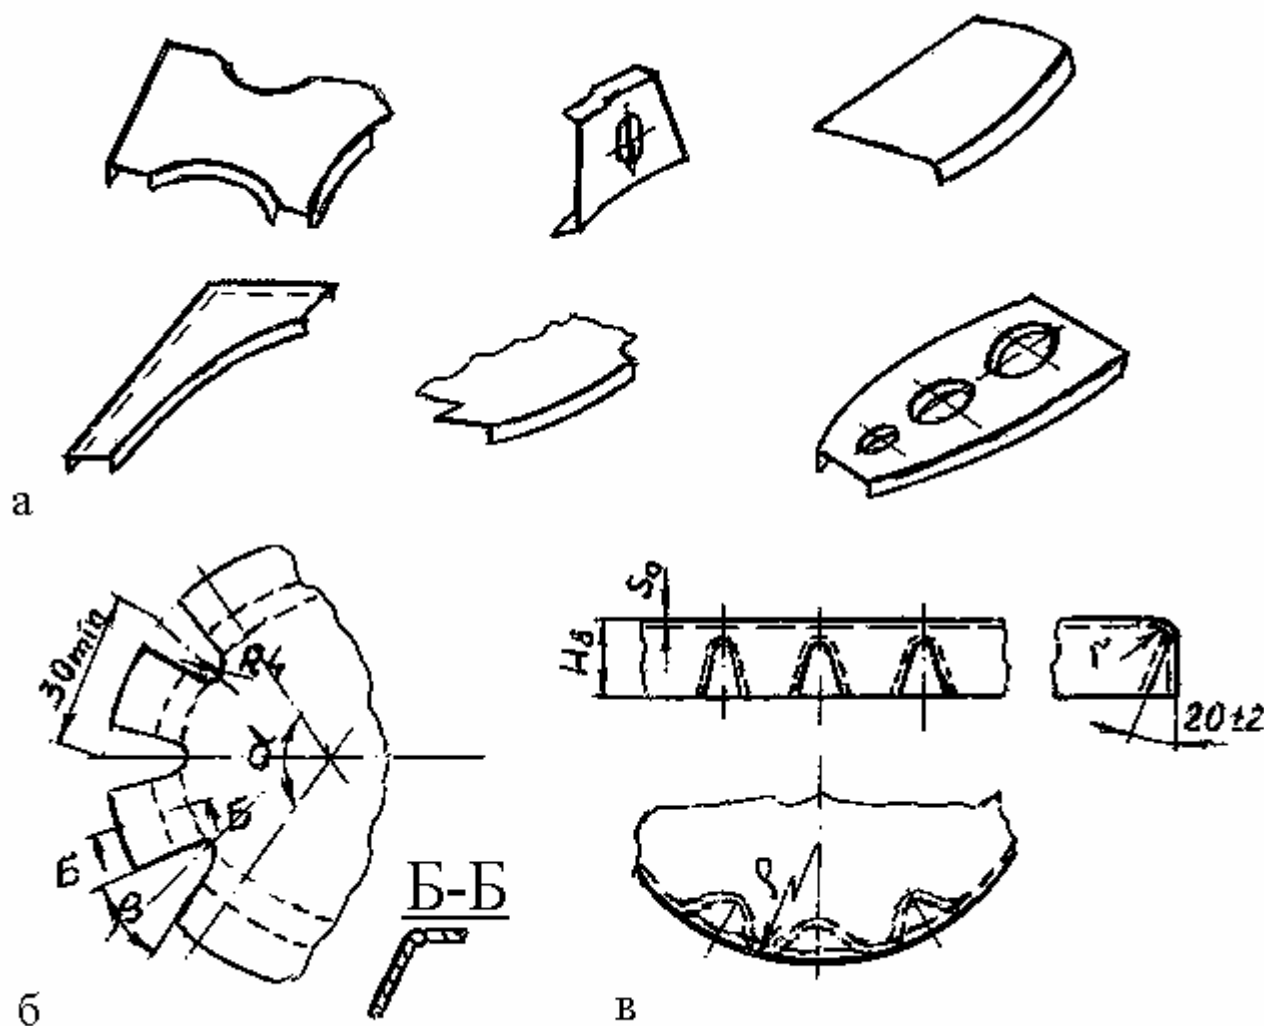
Типовые детали с криволинейными бортами: а – детали с плоскими стенками; б – с фестоными прорезными; в – с фестоными глухими
